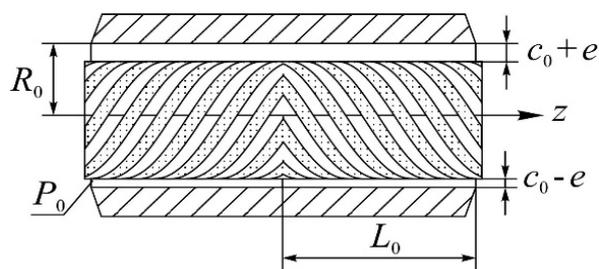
Радиальный газодинамический подшипник с шевронными канавками
